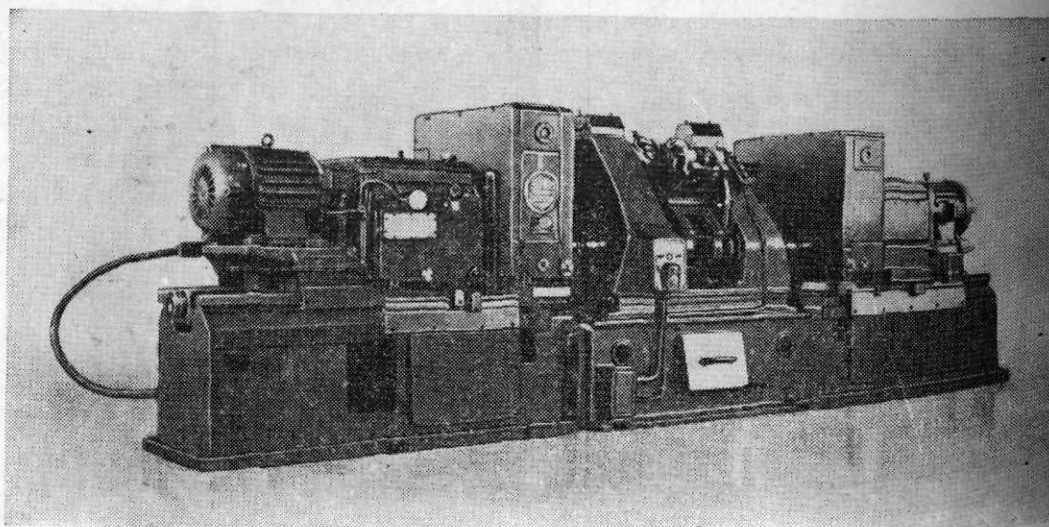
Специальный агрегатный станок типа 4Э32.
